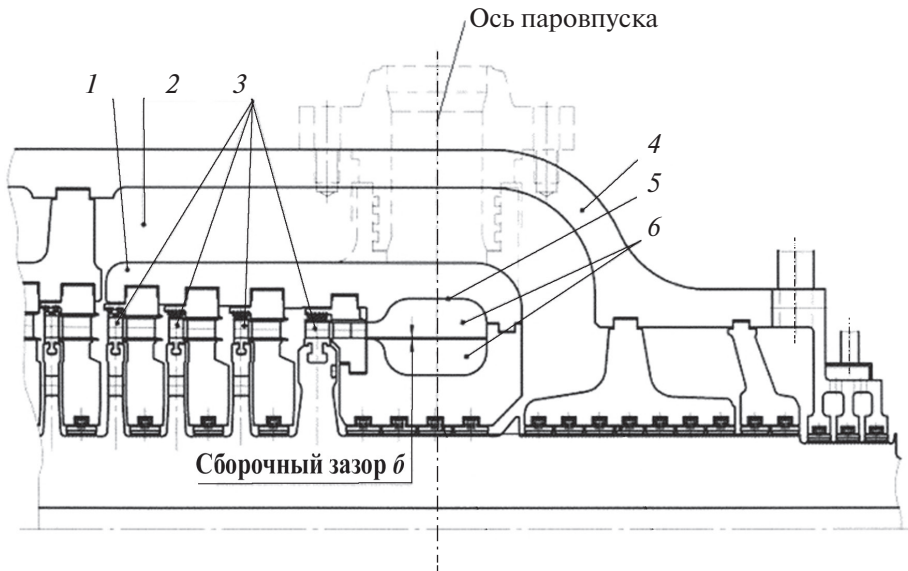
Часть высокого давления с регулирующим отсеком турбины Т-125/150-12,8: 1 — внутренний корпус ЦВД; 2 — межкорпусное пространство; 3 — нерегулируемые ступени давления; 4 — наружный корпус ЦВД регулирующего отсека; 5 — кольцевая камера паровпуска; 6 — перегородки
